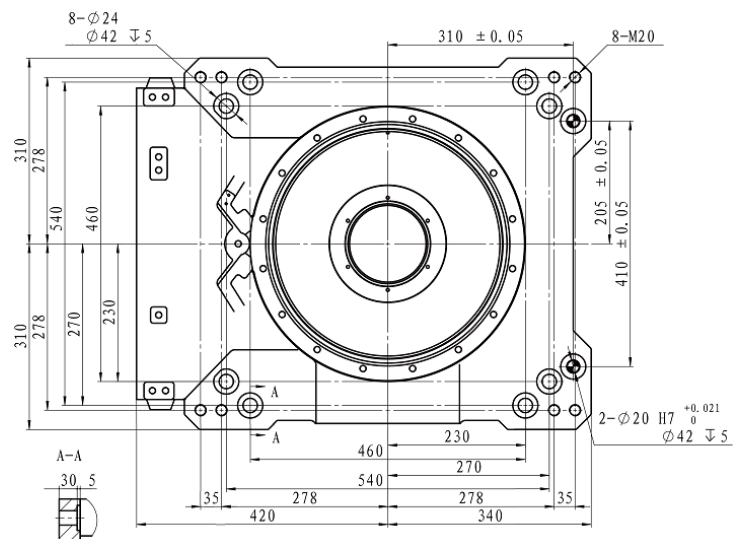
Габаритные чертежи робота-манипулятора SR60-2280B.
